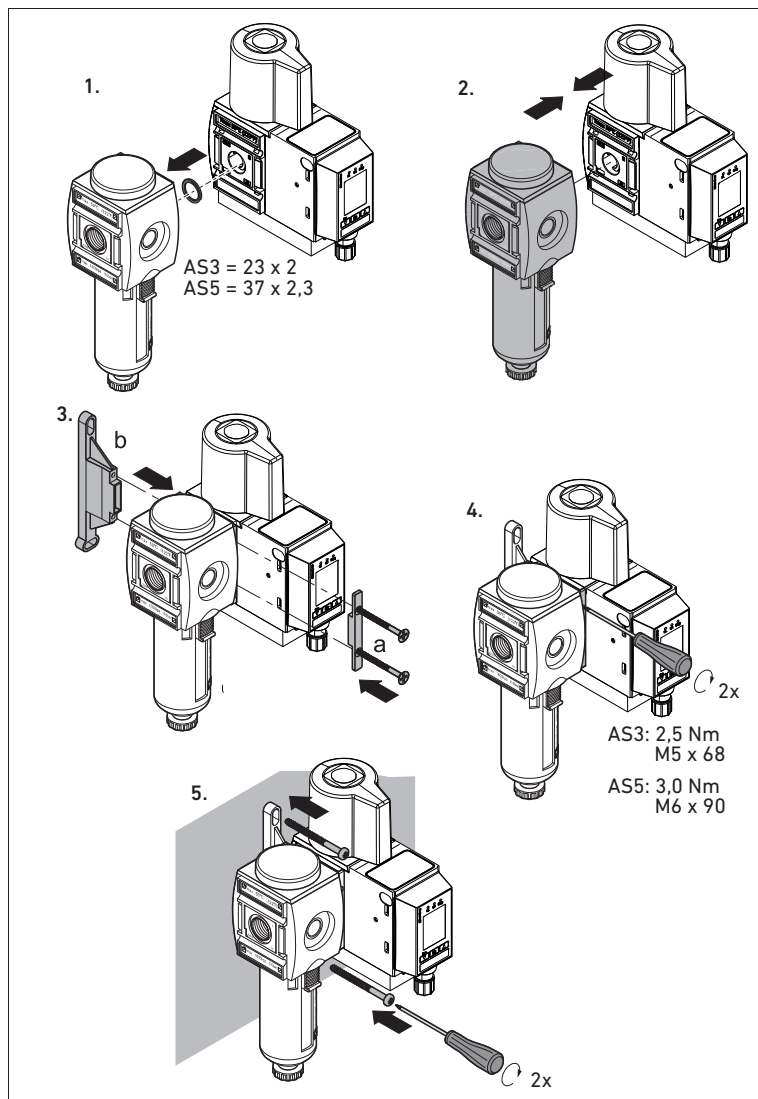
Fixation de l'EV1X à l'aide d'une fixation murale supplémentaire
